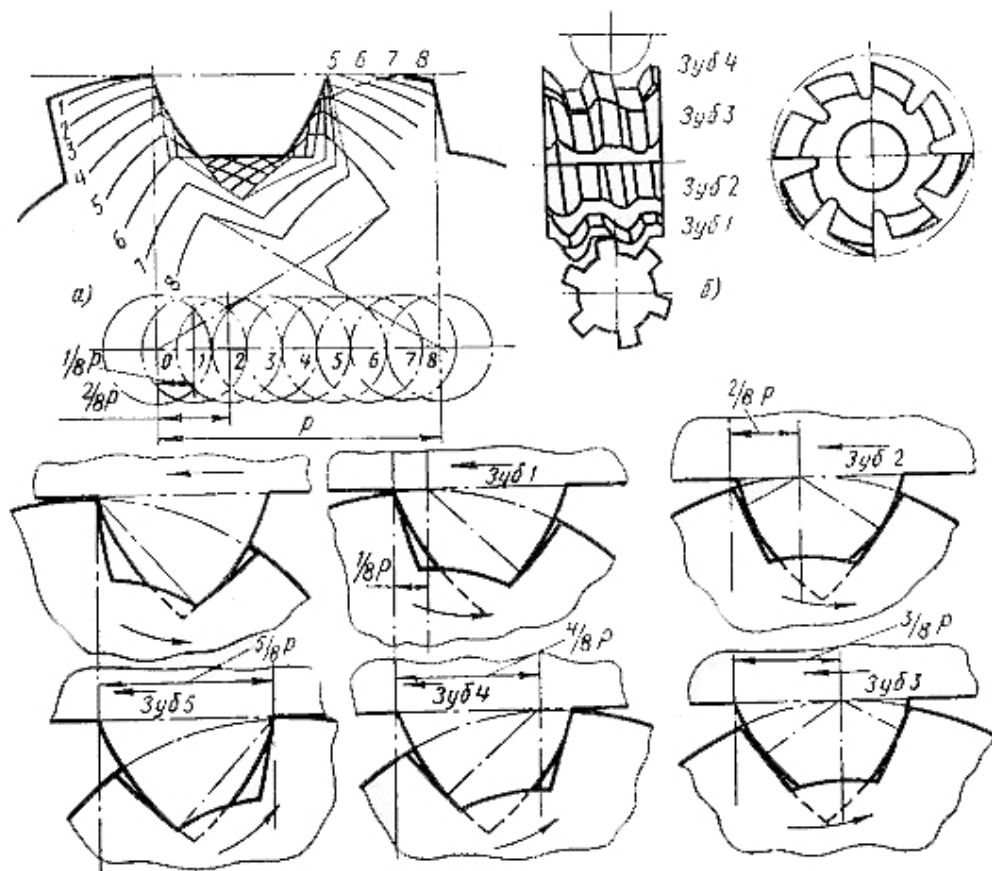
Схема роботи зубів фрези постійної установки [64]
